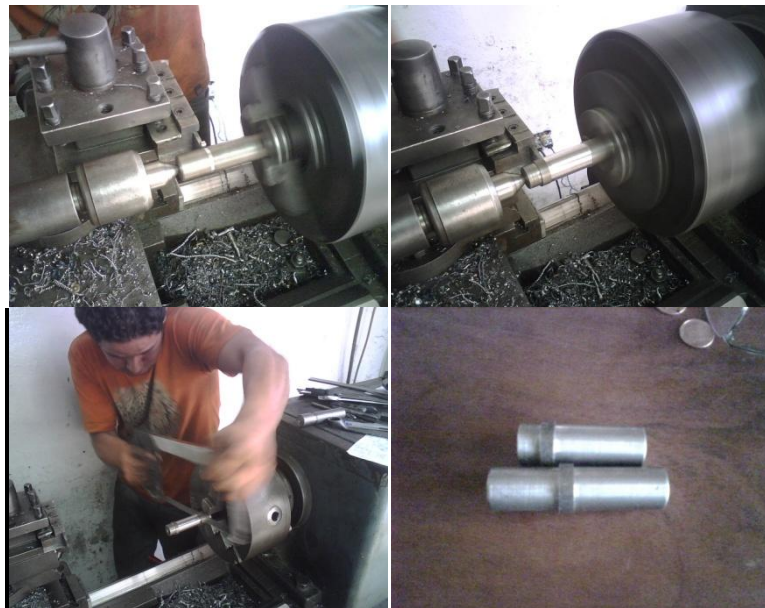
PROCESO DE CONSTRUCCIÓN DE LOS PIVOTES
